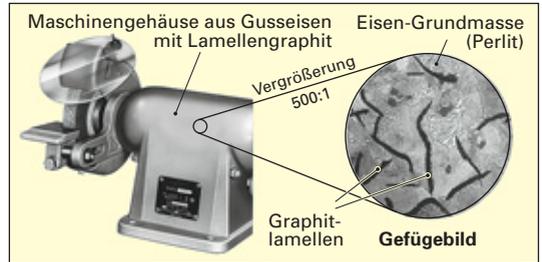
Schweißbockgehäuse aus Gusseisen mit Lamellengraphit
